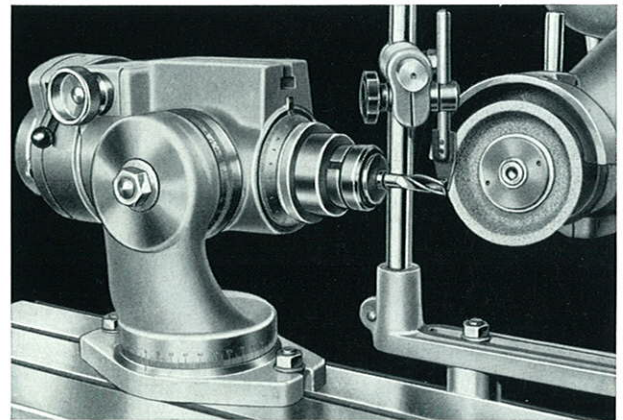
Schleifen eines spiralverzahnten Schaftfräasers mit HTR und Zahnstütze
